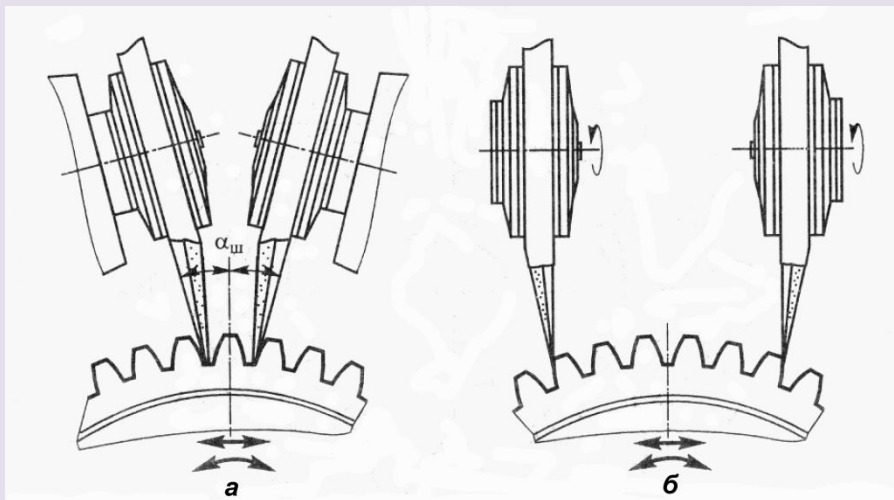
Схема установки тарельчатых шлифовальных кругов при обработке зубчатых колес:
